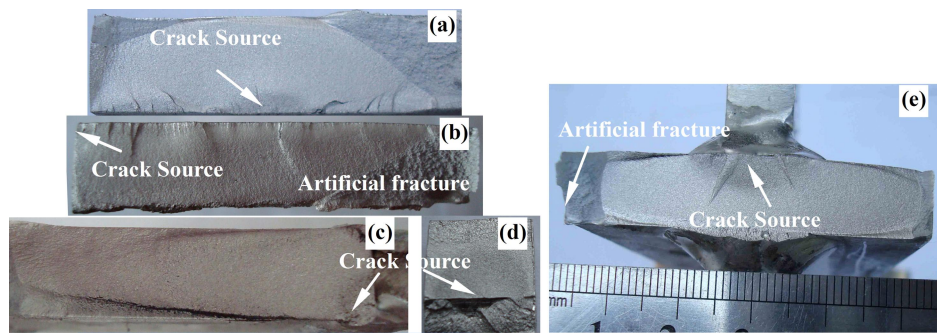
铝合金焊接接头疲劳断口宏观形貌
